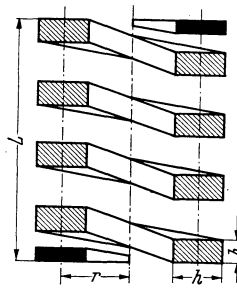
Zylindrische Schraubenfeder mit Rechteckquerschnitt.
